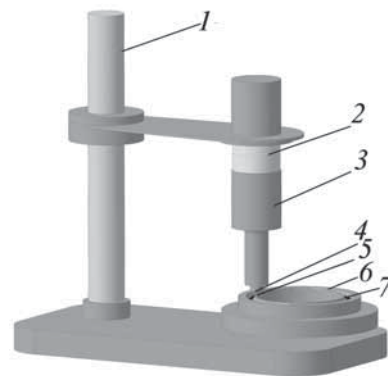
Схема обработки поверхностей дорожек качения подшипников:
